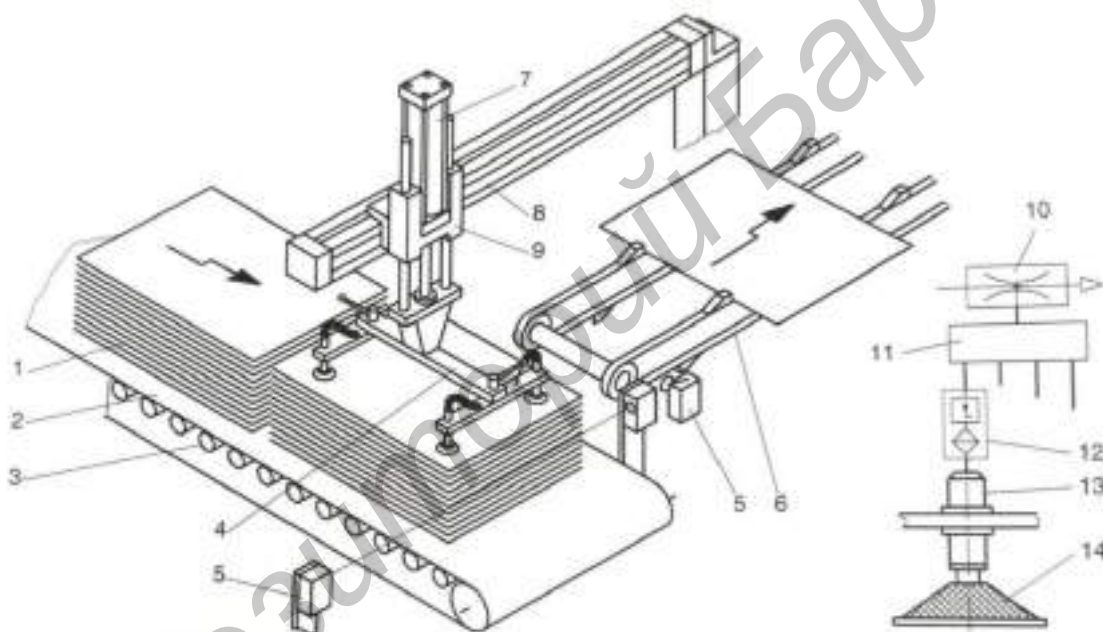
Общий вид и схема устройства для разгрузки древесных плит
